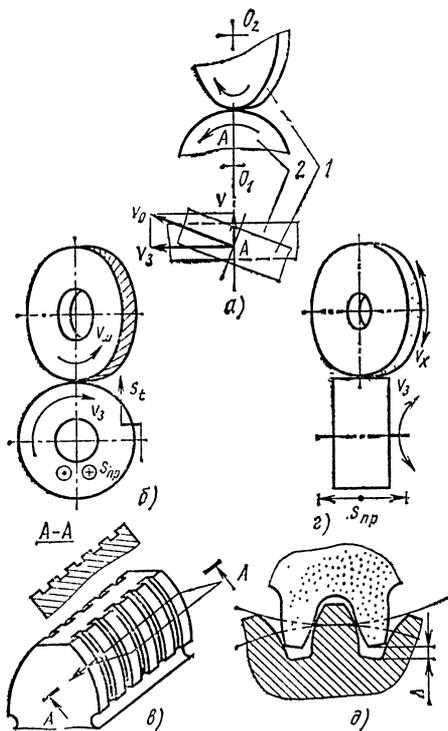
Схемы отделочной обработки зубьев зубчатых колес
